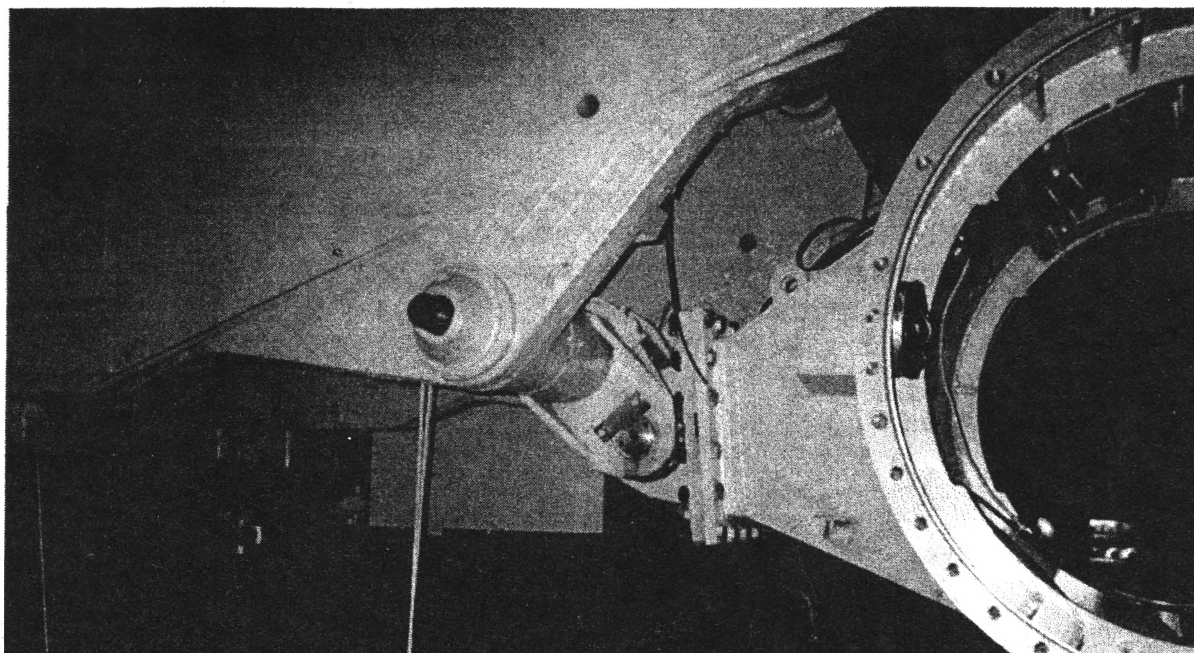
Рама карьерного самосвала «Катерпиллер» (США) с литыми элементами (затемнены крупные отливки)
